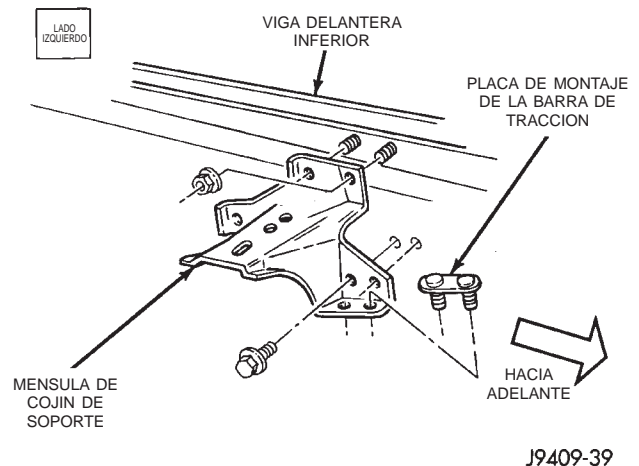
Ménsula de cojín de soporte—Lado izquierdo
